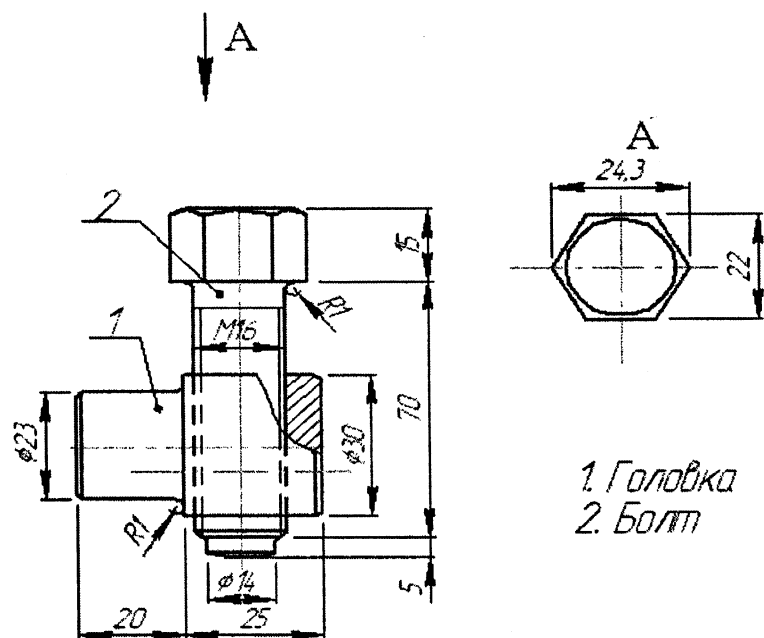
Приспособление для предварительного поджатия торцевой шайбы
